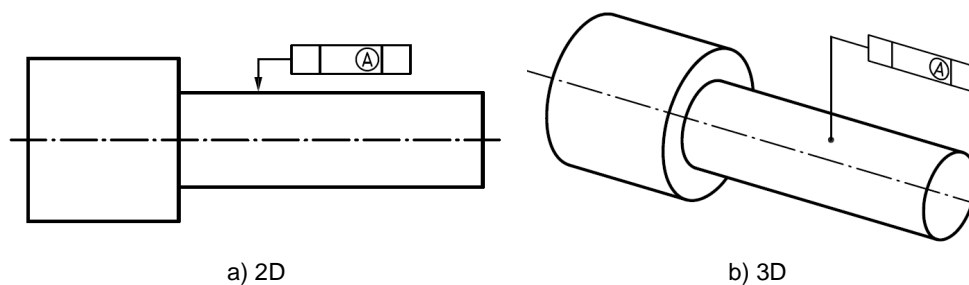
Exemplo de elemento toleranciado: linha mediana de superfície cilíndrica. Adaptada da ISO 1101
